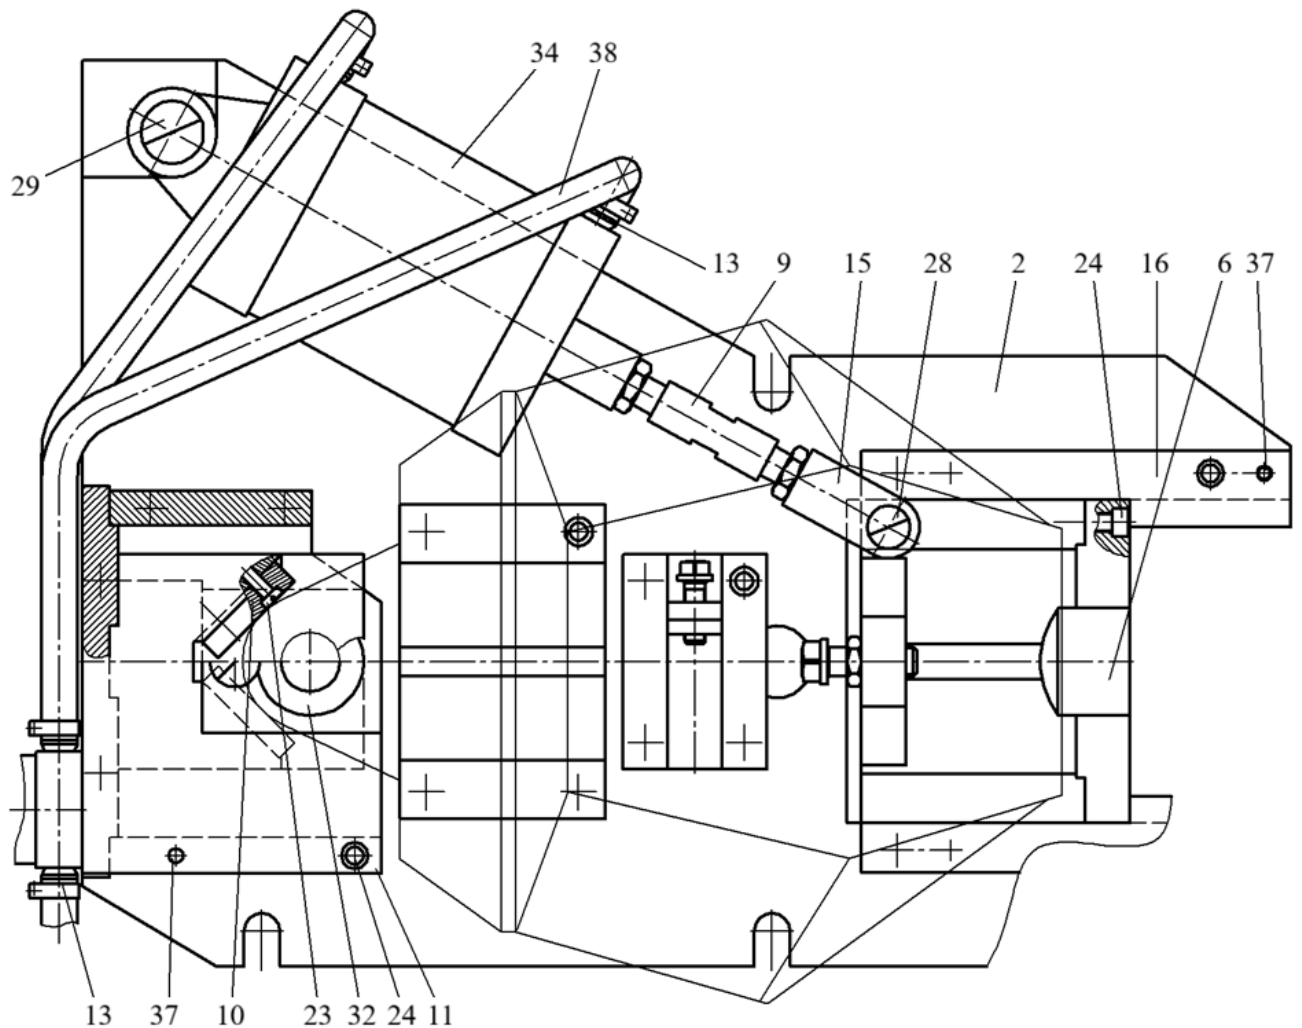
Кондуктор для свердління отвору Ø33H14
